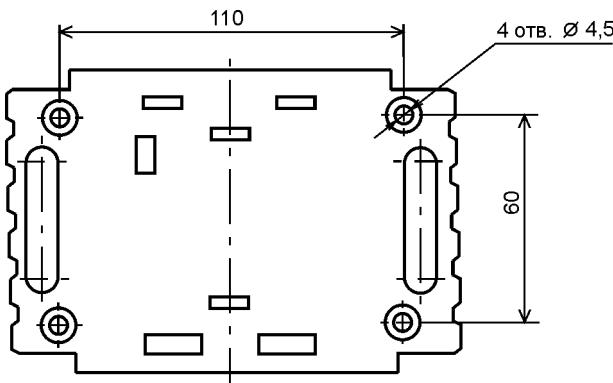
Крепление адресного блока (присоединительные размеры)
